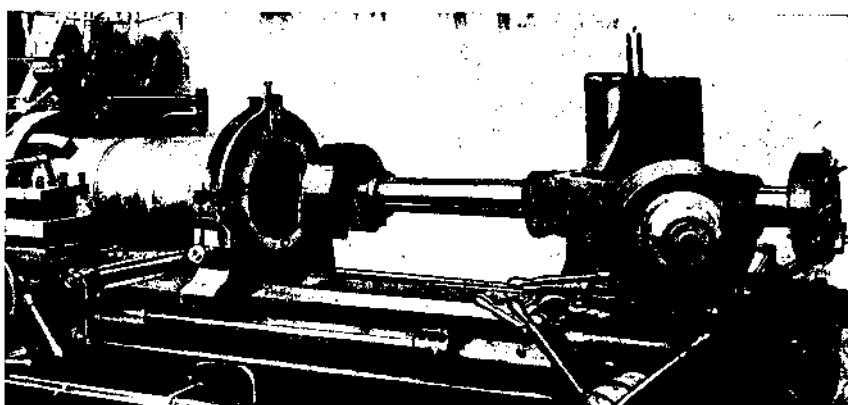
Обработка втулки двигателя Дизеля на револьверном станке.
